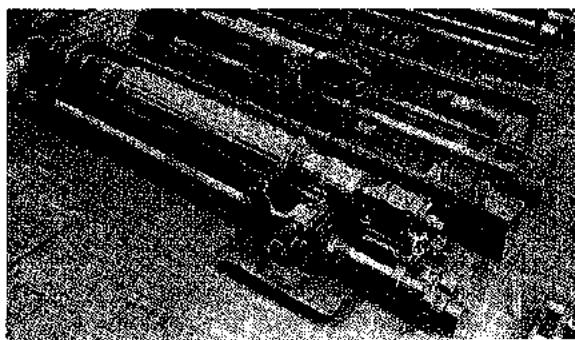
Estos tornos pueden mecanizar grandes piezas cuyo peso es de toneladas (R. K. LeBlond Machine Tool Co.)
